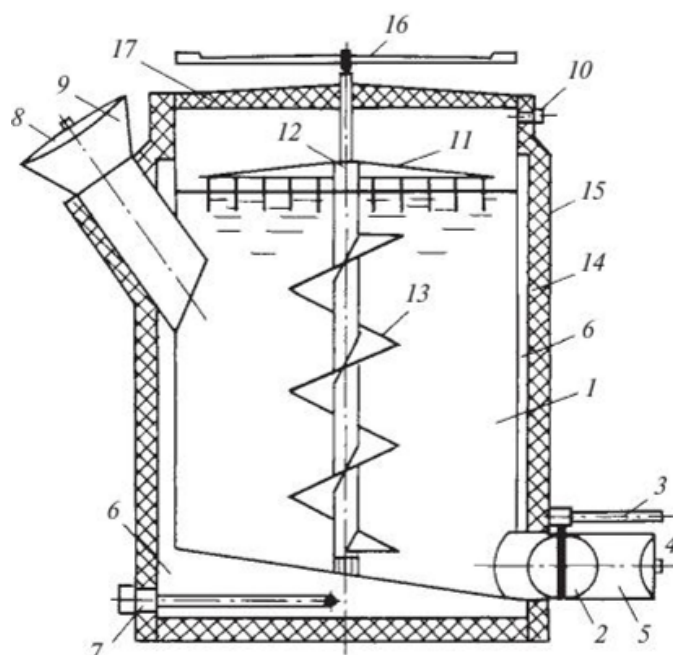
Схема биореактора-метантенка ИБГУ-1: 1 – корпус биореактора; 2 – диафрагма; 3 – рукоятка; 4,8 – затворы; 5 – шлюз для выгрузки сброженной массы; 6 – корпус тепловой рубашки; 7 – электронагреватель (ТЭН); 9 – загрузочный люк; 10 – газовый штуцер; 11 – гребенка; 12 – вал мешалки; 13 – шнек; 14 – облицовка теплоизоляции; 15 – теплоизоляция; 16 – рукоятка-крестовина мешалки; 17 – крышка биореактора
